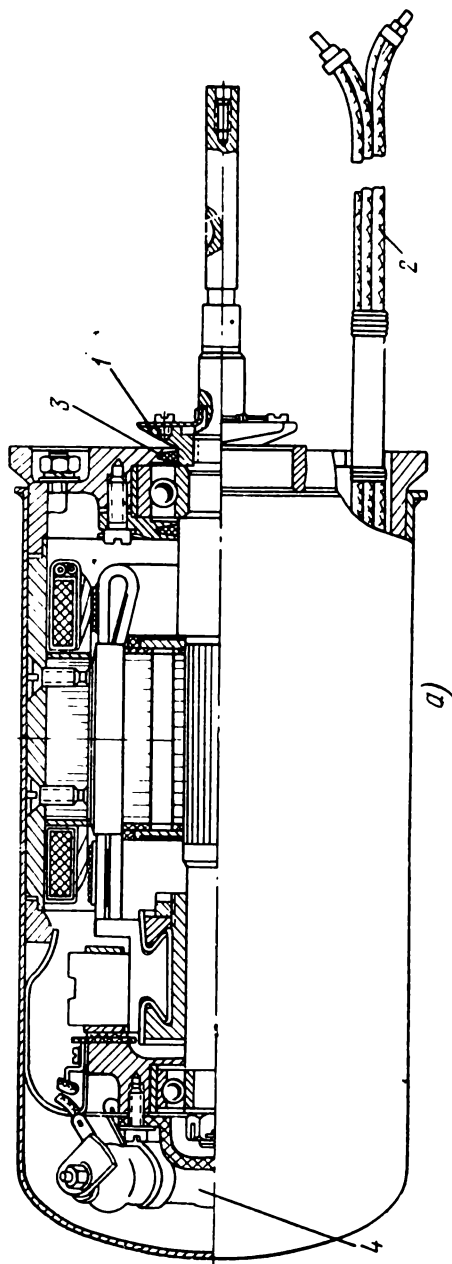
12. Типовая конструкция двигателя для привода внутрибакового ЭЦН:
